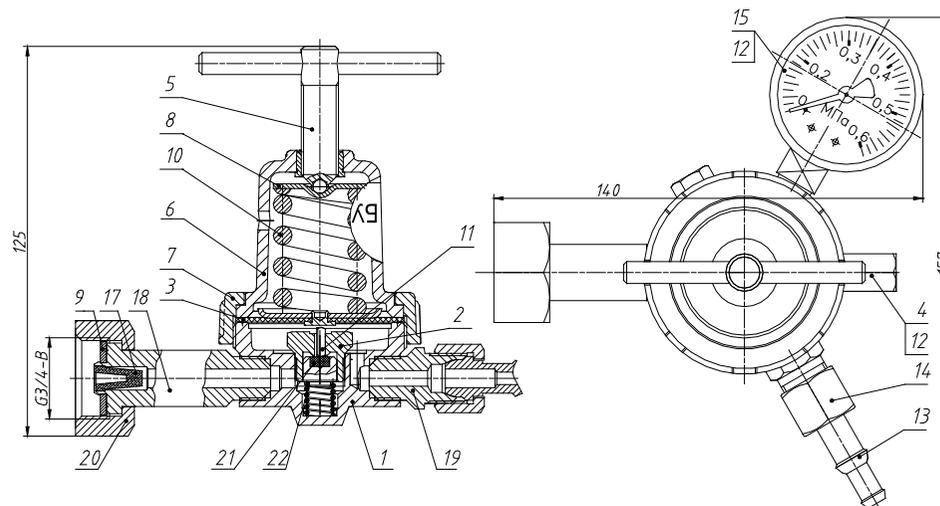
Редуктор баллонный углекислотный одноступенчатый:
